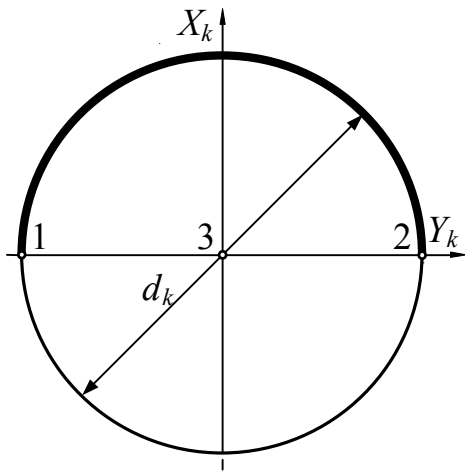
Схема расчета опорных точек профиля круглой СМП
